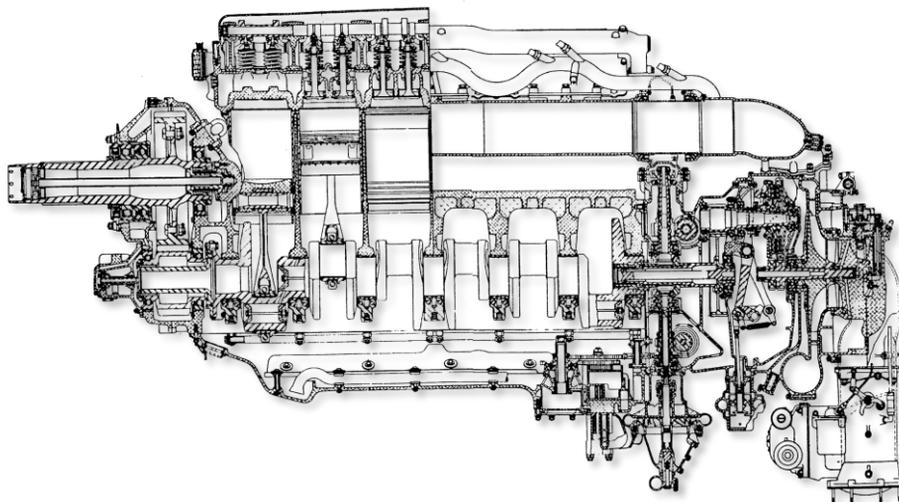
Схематический вид двигателя Packard Merlin V-1650
